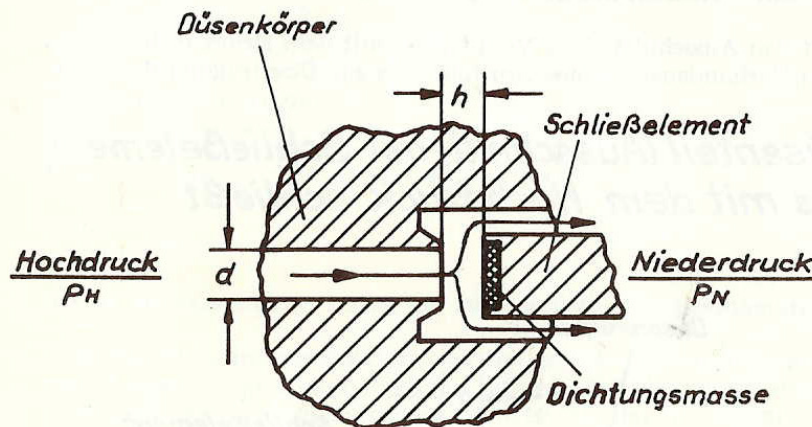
Düsenteil (Ausschnitt) mit gegen den Hochdruck dichtendem Schließelement
